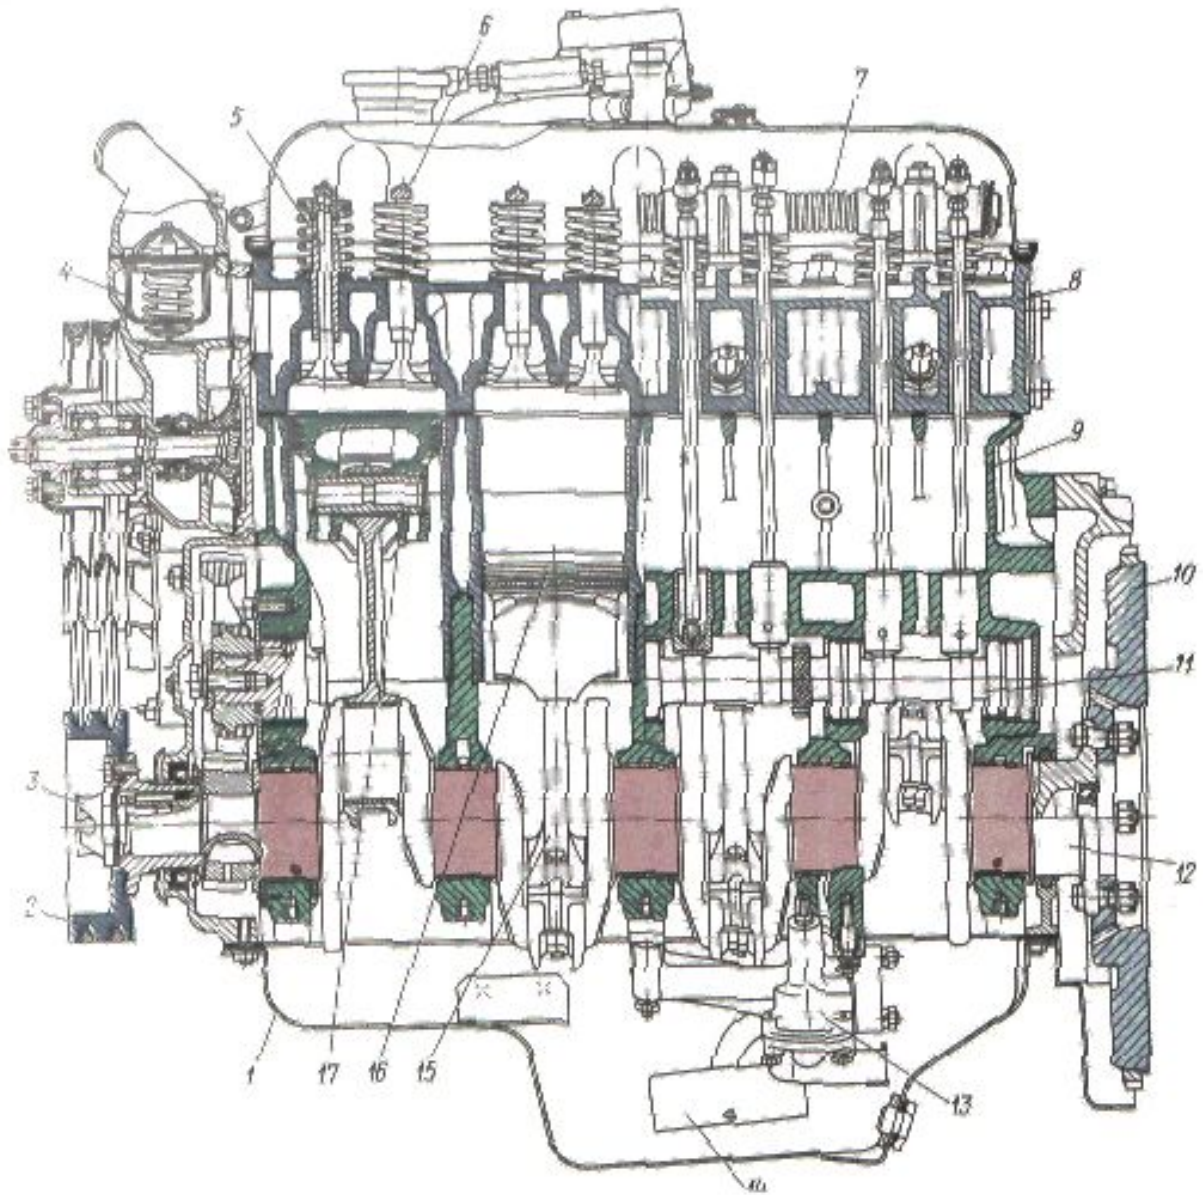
Продольный разрез двигателя автомобиля ГАЗ-24 "Волга":
